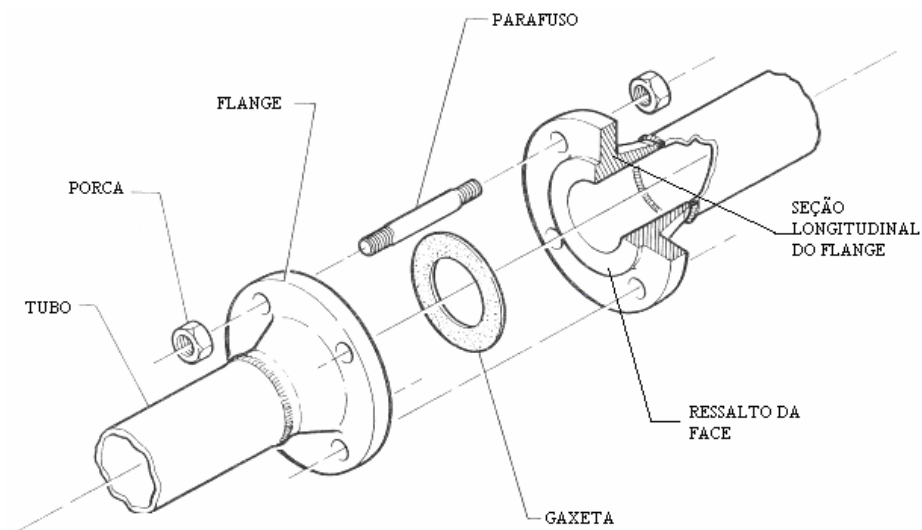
Componentes principais da junta flangeada com gaxeta circular
